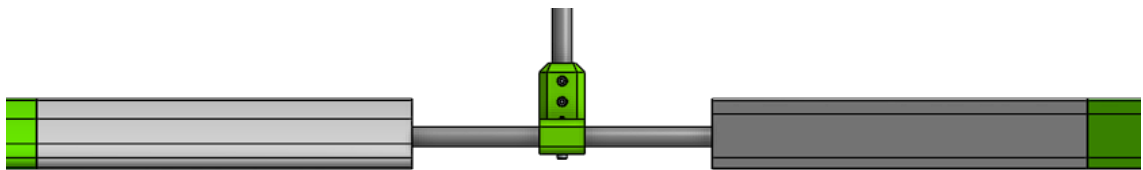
Vista frontal del ensamblaje de la hélice en Onshape [fuente: elaboración propia]
